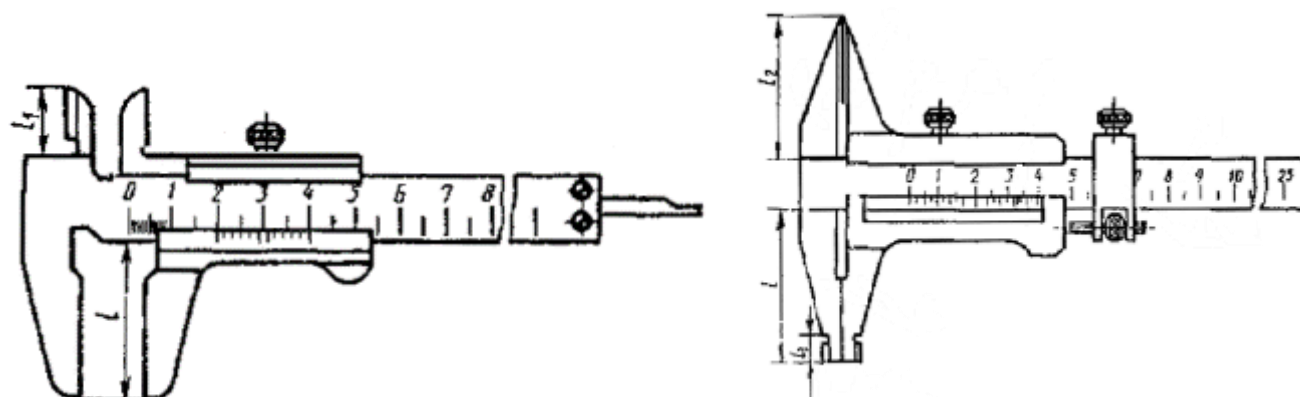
Обозначение вылета губок для измерений наружных и внутренних размеров
